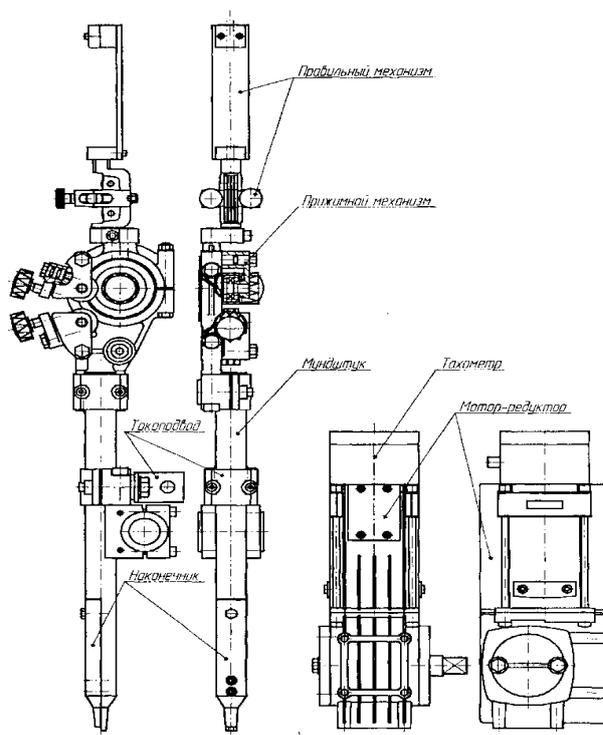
Сварочная головка А6 «TwinArc»
